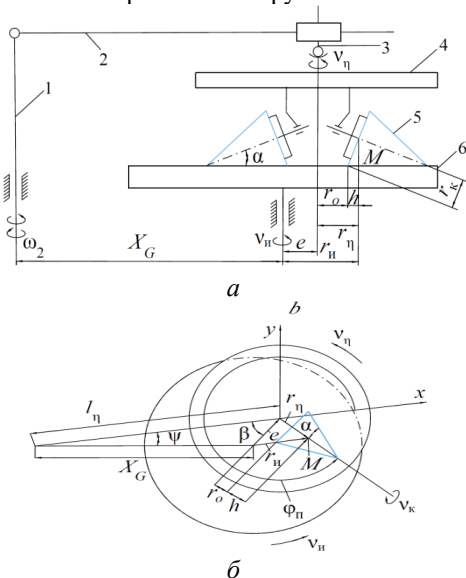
Схема обработки деталей с коническими поверхностями (а) и размерная цепь ее рабочей зоны (б)
